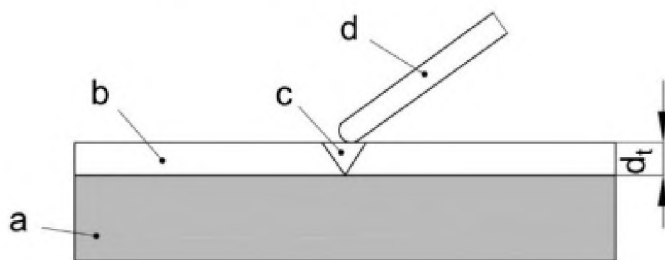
Стыковое сварное соединение, где a – подложка, b – термопластичный лист, c – сварной шов, d – электрод
